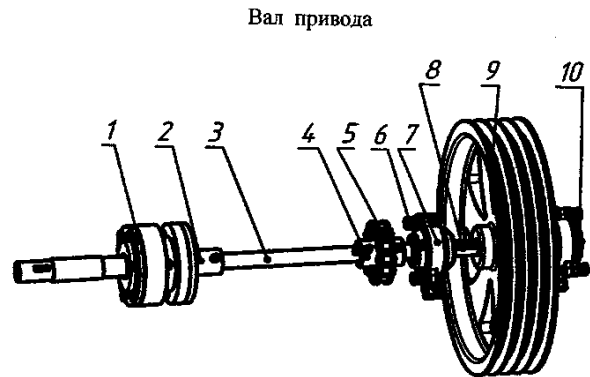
Вал привода КИР.23.0.0000-02:
